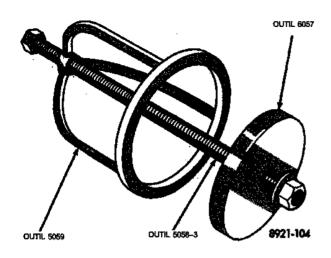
Outil compresse-ressort de gamme basse/marche arrière
